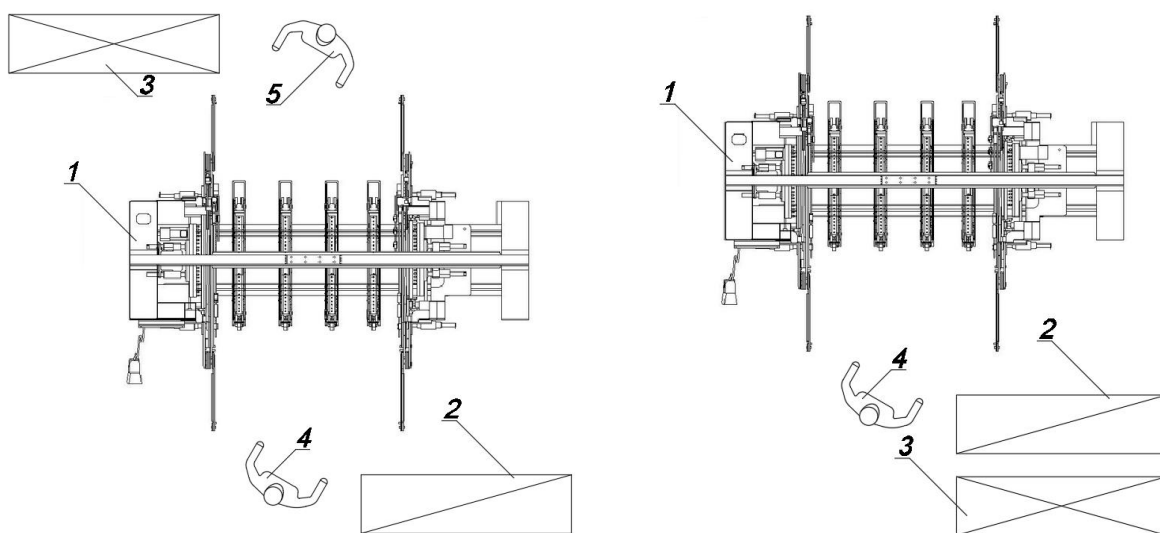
Схеми організації робочого місця біля автоматичного багатошпindelного свердлильно-присаджувального верстата: 1 – автоматичний багатошпindelний свердлильно-присаджувальний верстат, 2 – підступне місце для деталей до обробки, 3 – підступне місце для деталей після обробки, 4 – оператор, 5 – допоміжний працівник
